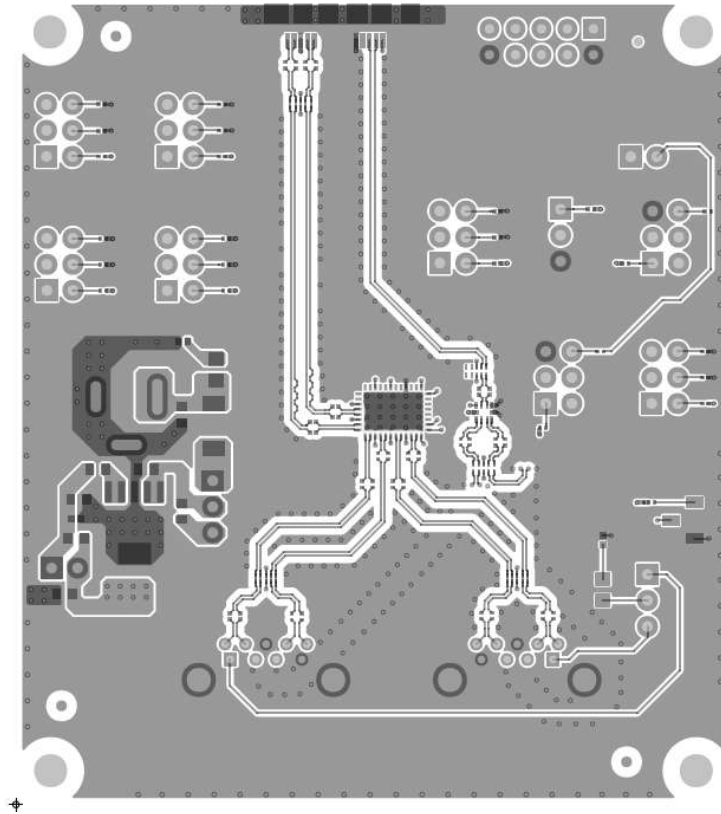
TUSB521Q1-EVM PCB 第 1 层 (顶部)
